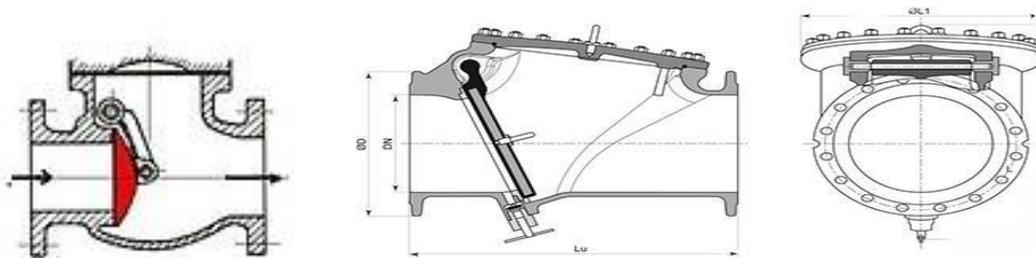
Schéma d'un Clapet d'anti-retour.
